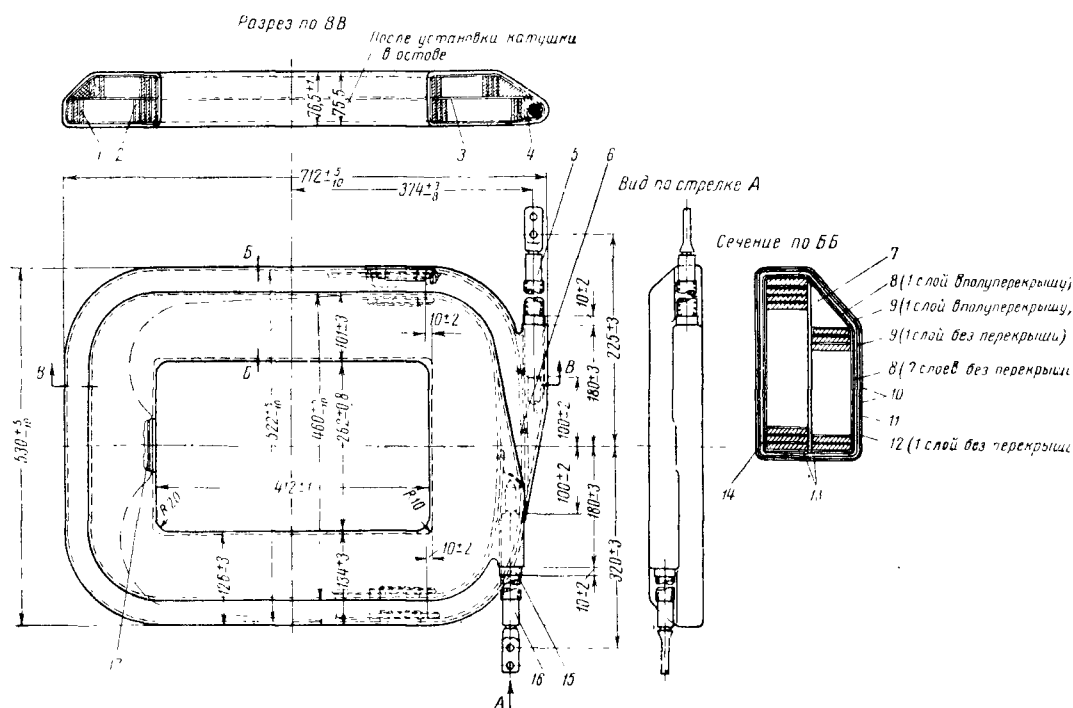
Катушка обмотки якоря двигателя типа НВ-406А
